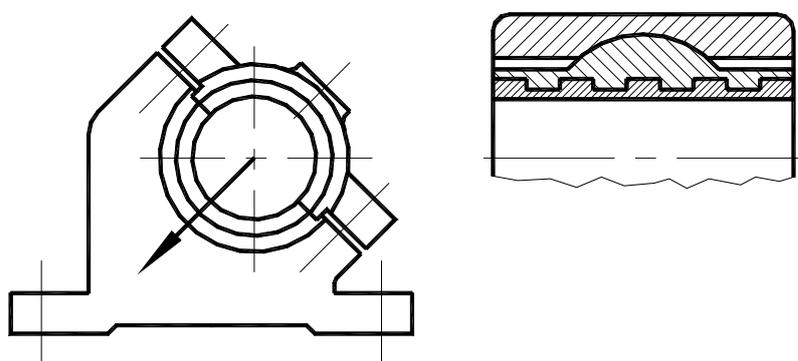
Разъемный самоустанавливающийся подшипник
